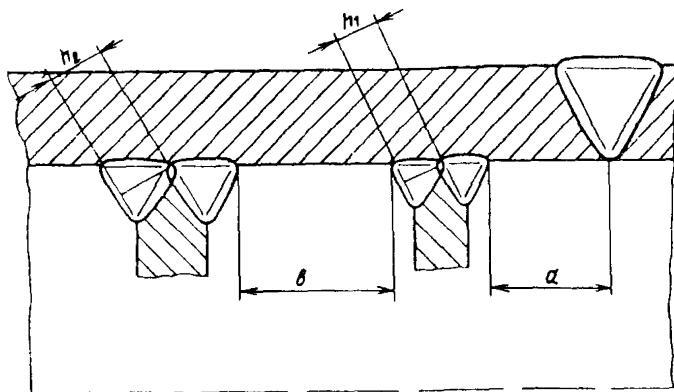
Расположение сварных швов приварки деталей к поверхностям оборудования и трубопроводов
